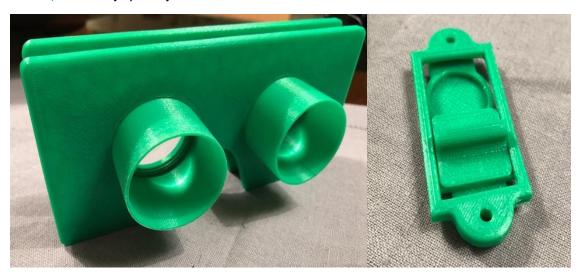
y 84: Captura del resultado de la impresión del Equipo Ocular y el Equipo del Botón tras su montaje
